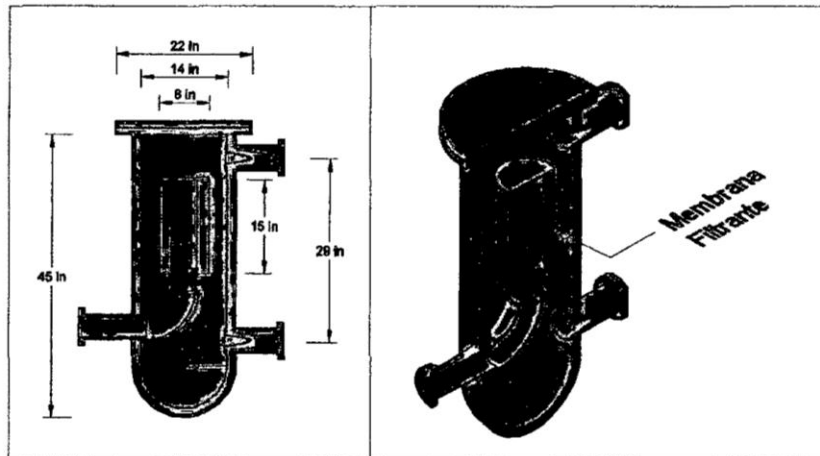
Diseño Filtro coalescente Punto de Custodia "Caldas Viejo".
